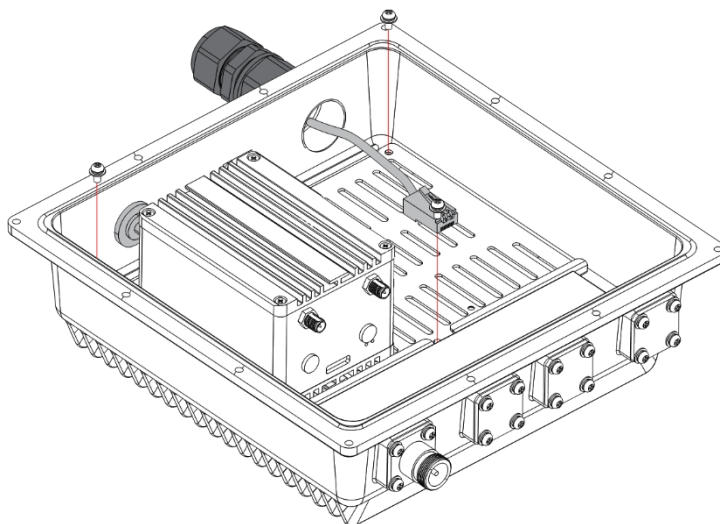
□ Befestigung der Montageplatte im Gehäuse
